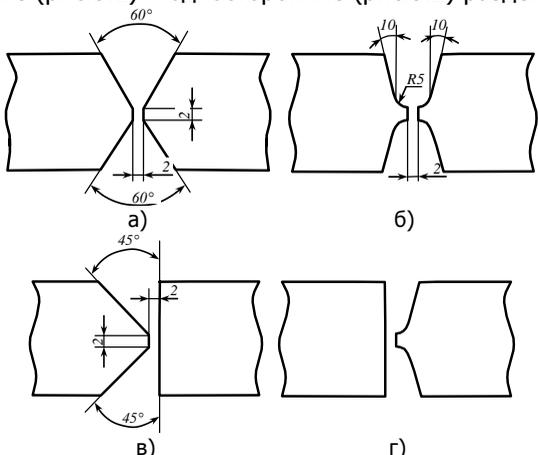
Двухсторонние разделки кромок под сварку:
